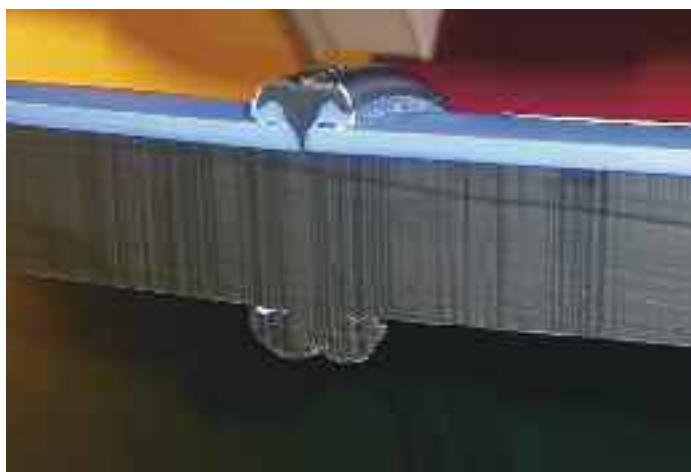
Сварка встык труб ПРОТЕКТ без удаления защитного покрытия.
